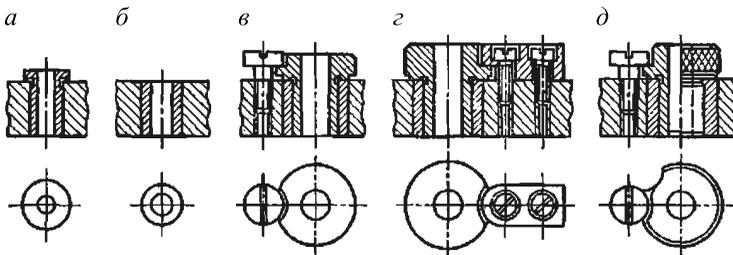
Неподвижные вращающиеся кондукторные втулки
